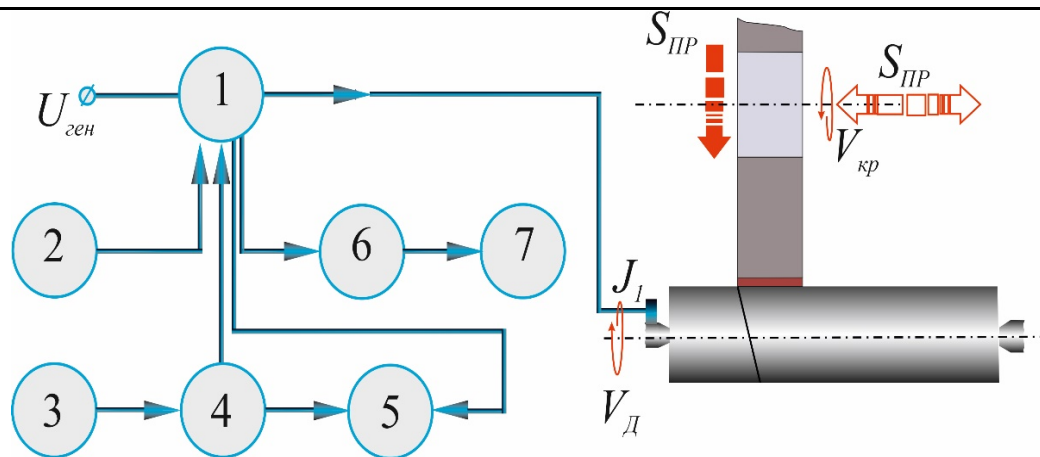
Схема устройства для контроля времени контакта шлифовального круга с заготовкой:
